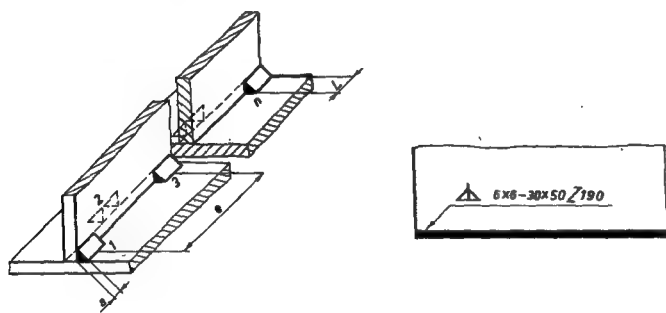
Representación unificada de soldadura con cordón interrumpido en zigzag, sobre chapa de espesor $a = 6$ mm, con $n = 30$ costuras de longitud $L = 50$ mm y paso $e = 190$ mm.
